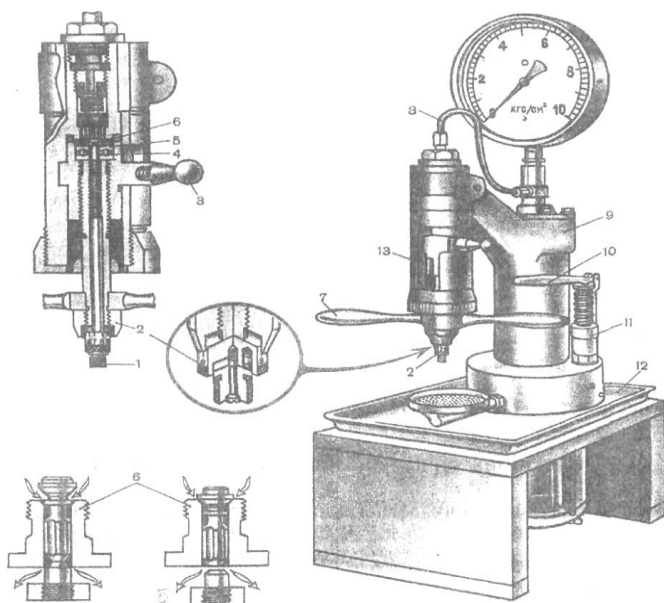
Прилад КИ-1086 для випробування нагнітальних клапанів: 1 – мікрометричний гвинт; 2 – гайка з поділками; 3 – рукоятки установлення клапану; 4 – упорний підшипник; 5 – кільце; 6 – клапан з прокладкою, що випробуються; 7 – рукоятка; 8 – трубка; 9 – корпус приладу КИ-1086 ГОСНИТИ; 10 – рукоятка підкачки палива; 11 – підкачуючий насос; 12 – піддон; 13 – пристрій для кріплення нагнітального клапану.
